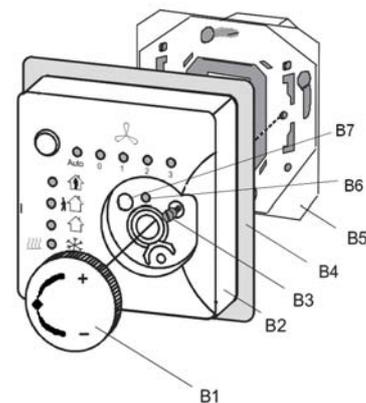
Montage des Fan-Coil Unit Bediengerätes
